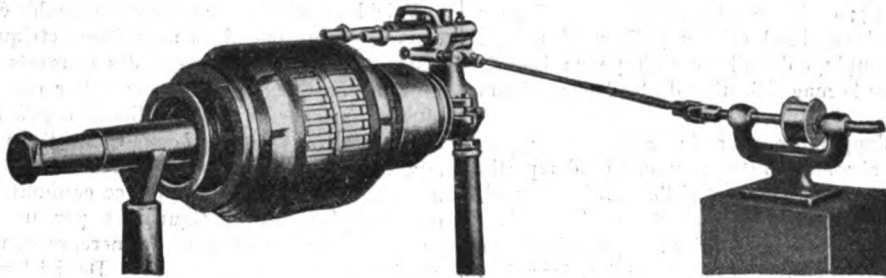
Machine à rainurer les collecteurs; type portable en service.
